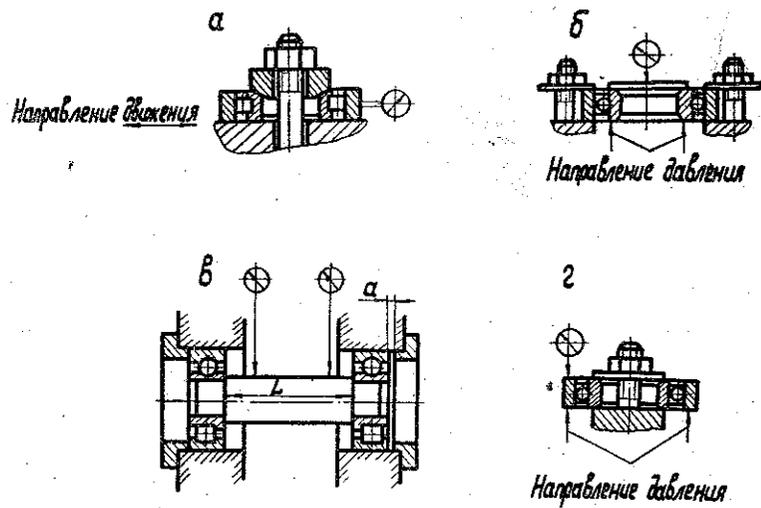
Схемы определения радиального и осевого зазора подшипников качения
